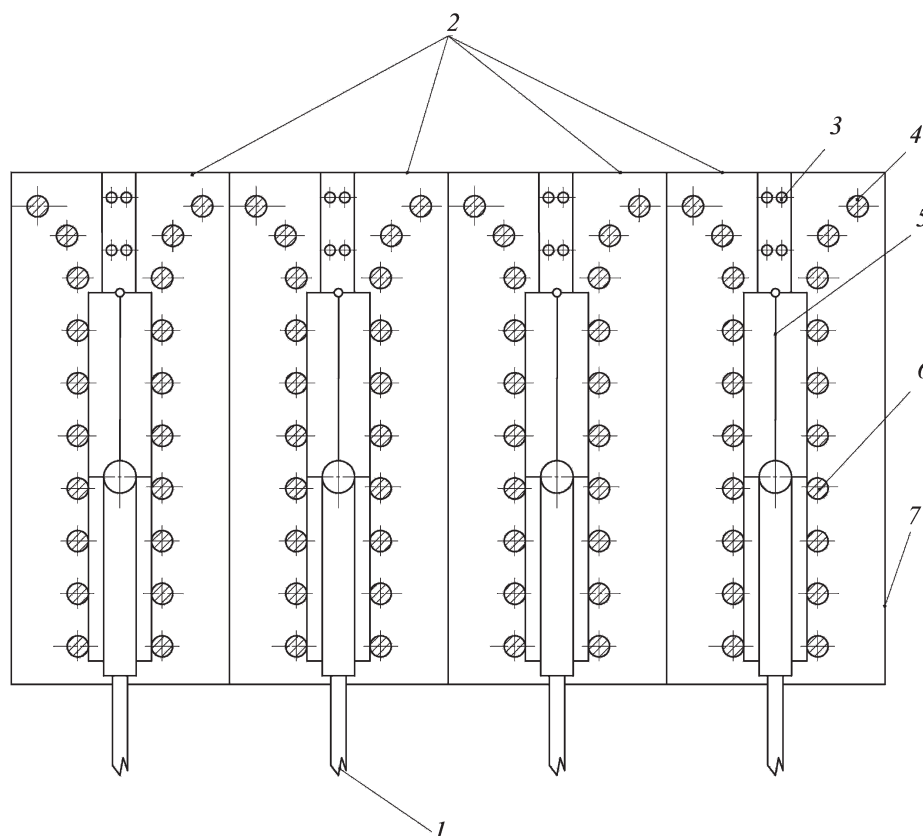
Общий вид модульного подложкодержателя с насадками-рамами с раскрывающейся и поворотной подложконесущей поверхностью:
